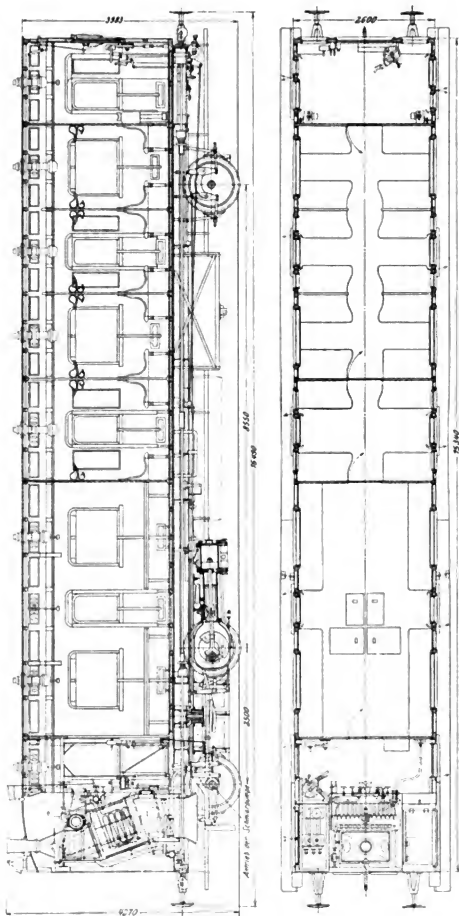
Dreilachsiger Dampfwagen der Preussischen Staatseisenbahn nach Stolz.
